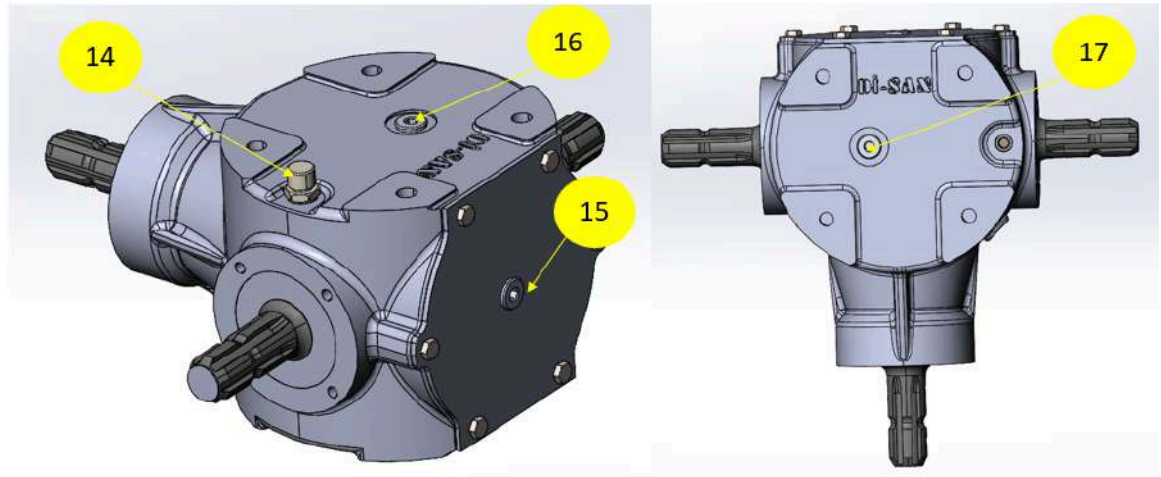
Пробки редуктора: 14 - сапун; 15 - контрольна пробка рівня мастила; 16 - заливна пробка; 17 - зливна пробка (вид спереду)
